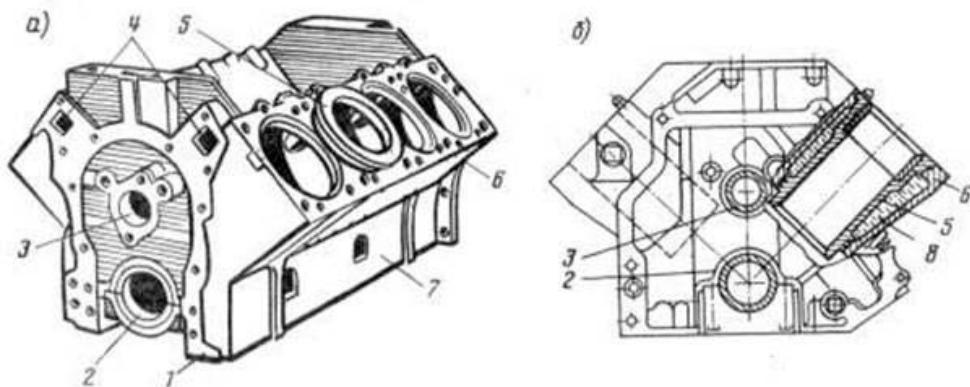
Блок цилиндров V- образного силового агрегата:
